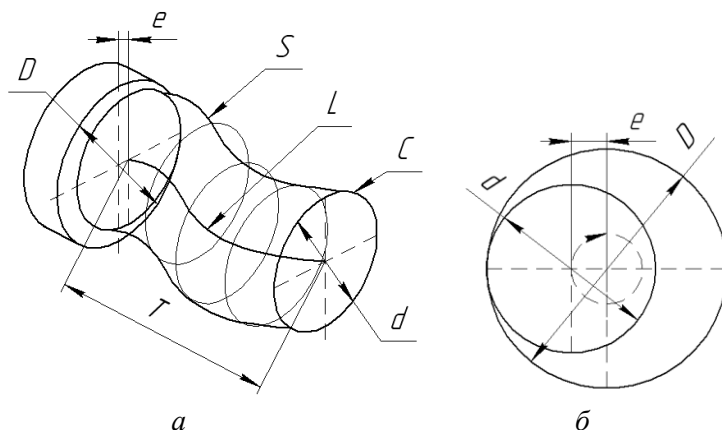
Геометрия круговой винтовой поверхности ротора насоса: a – общий вид; b – поперечное сечение.
